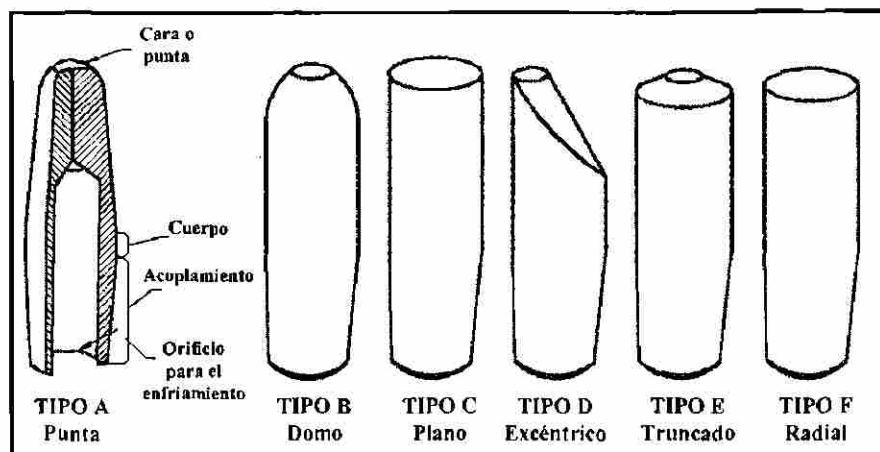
Geometrías de electrodos para soldadura por puntos ⁽³⁵⁾.
